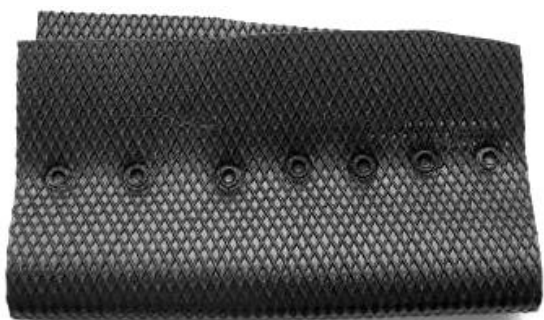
Сформированные сварные швы лент георешетки.
